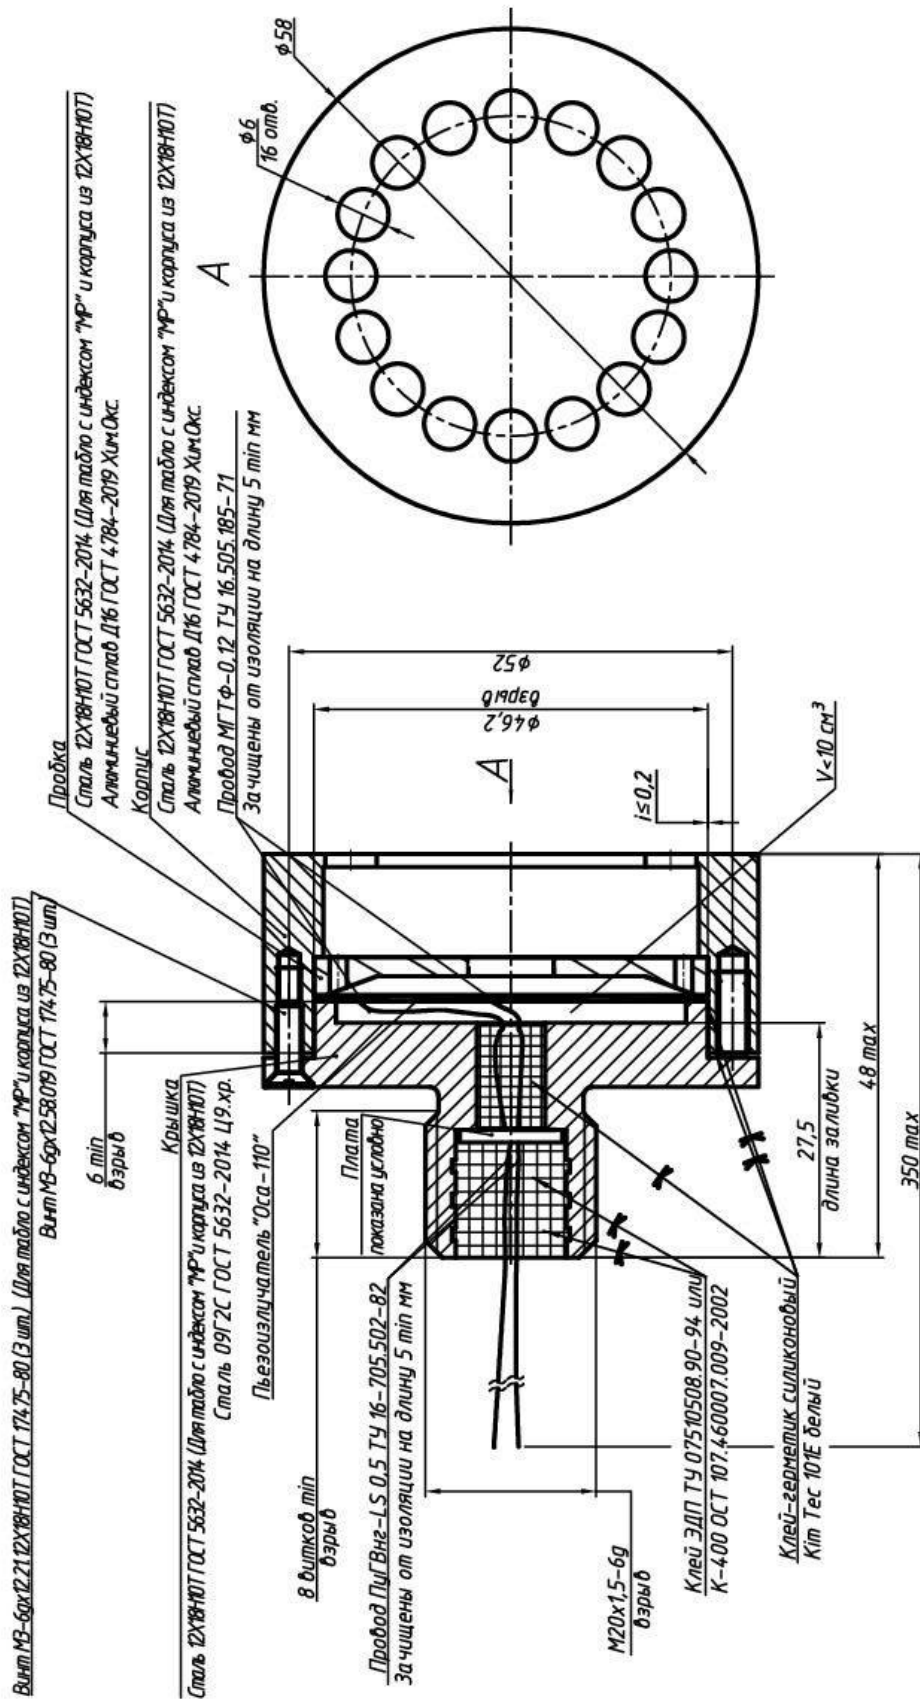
Звуковой излучатель для Филлин-Т-А или Филлин-Т-Н с резьбой М20х1,5
